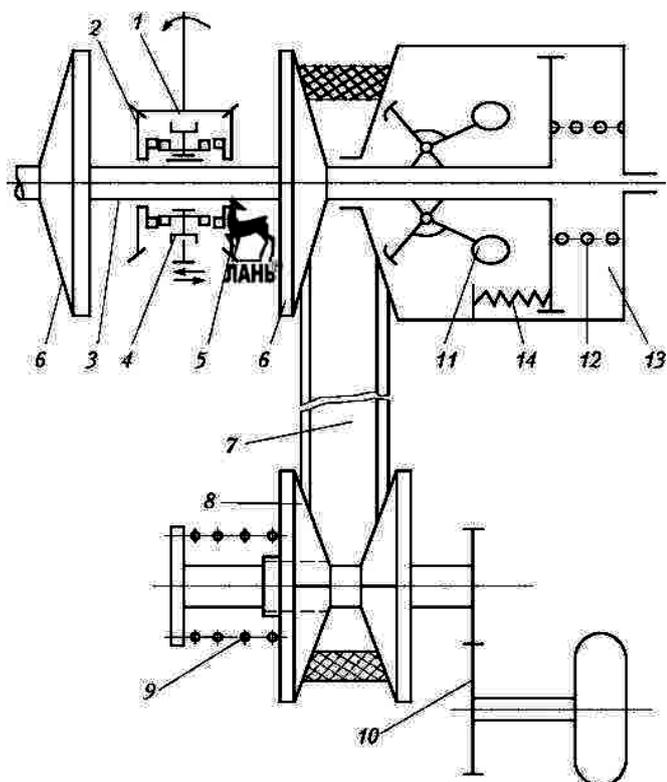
Клиноременная передача: 1-ведущая шестерня; 2, 5 — шестерни; 3 — вал; 4- кулачковая муфта; 6 — ведущий шкив вариатора; 7 — ремень; 8 — ведомый шкив; 9, 12, 14 — пружины; 10-цилиндрическая передача; 11-центробежный регулятор; 13 — цилиндр.
